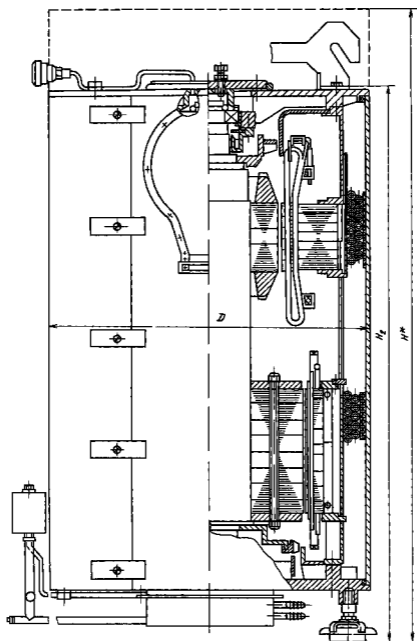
Габаритные и установочно-присоединительные размеры преобразователей ППЧВ
